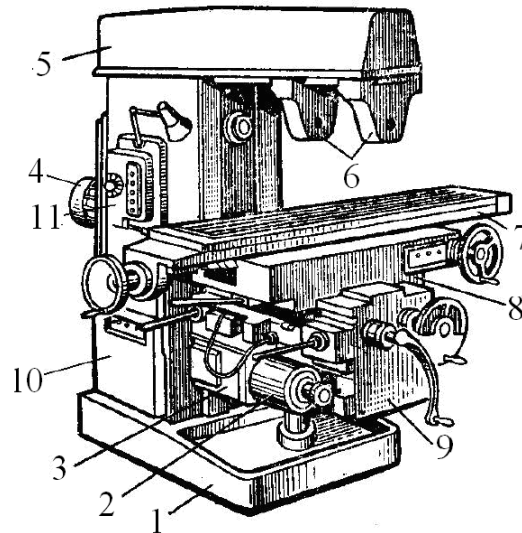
Загальний вигляд горизонтально-фрезерного верстата:
